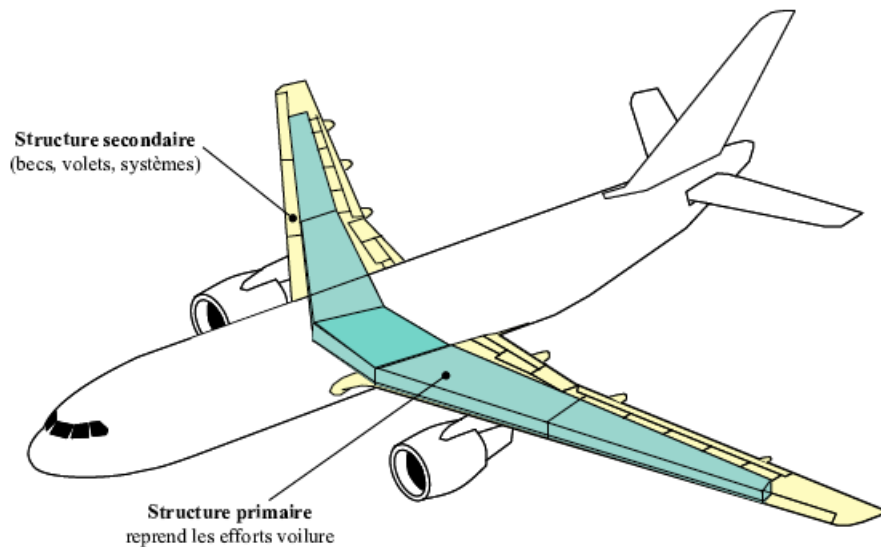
Structures primaire et secondaire d'une voilure
